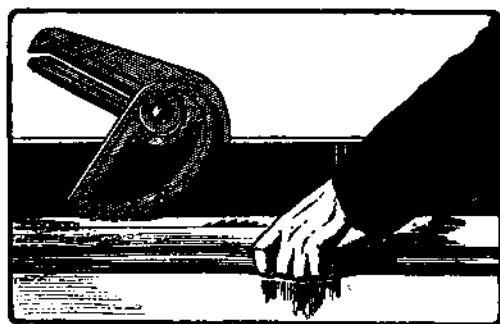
Приспособление против отбрасывания дерева в виде качающегося рычага.
